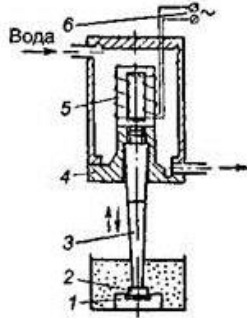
Схема ультразвуковой установки для механической обработки заготовок: 1-заготовка; 2-инструмент; 3-акустический концентратор; 4-вибрирующая головка; 5-магнитострикционный преобразователь (вибратор); 6-генератор ультразвуковых частот.
